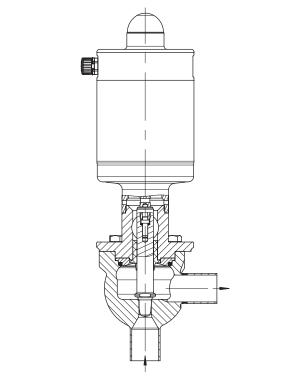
Stellventil Typ 3347/3379 mit Anschweißenden Vollmaterialausführung mit angeflanschtem Oberteil
